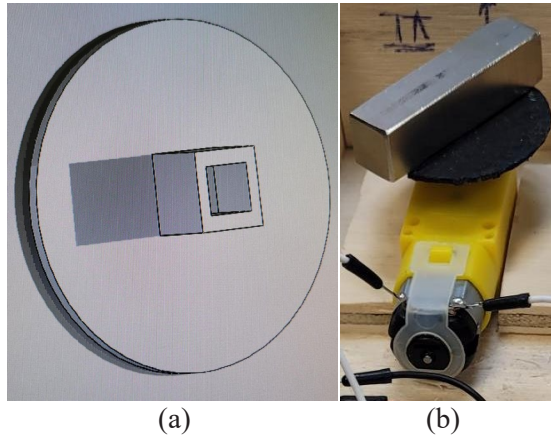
(a) Pieza de acoplamiento. (b) Vista del montaje del imán con el motor.
